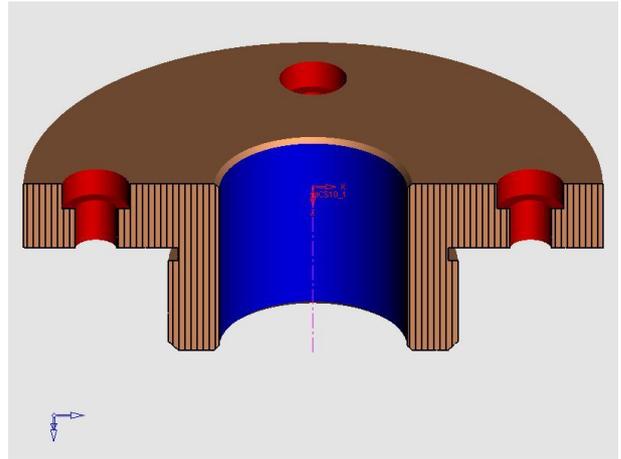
Модель заготовки, обрабатываемой на сверлильной операции
